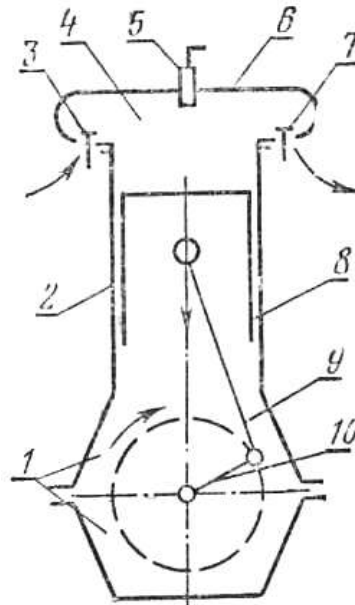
Принципиальная схема поршневого двигателя внутреннего сгорания: 1 — картер; 2 — цилиндр; 3 — впускной клапан; 4 — камера сгорания; 5 — свеча зажигания (или форсунка); 6 — головка цилиндра; 7 — выпускной клапан; 8 — поршень; 9 — шатун; 10 — кривошип
